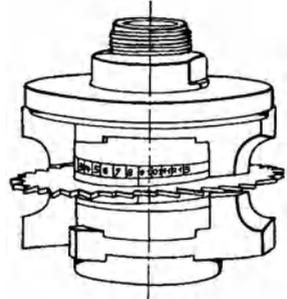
Zusammengesetztes Fräserwerkzeug.
